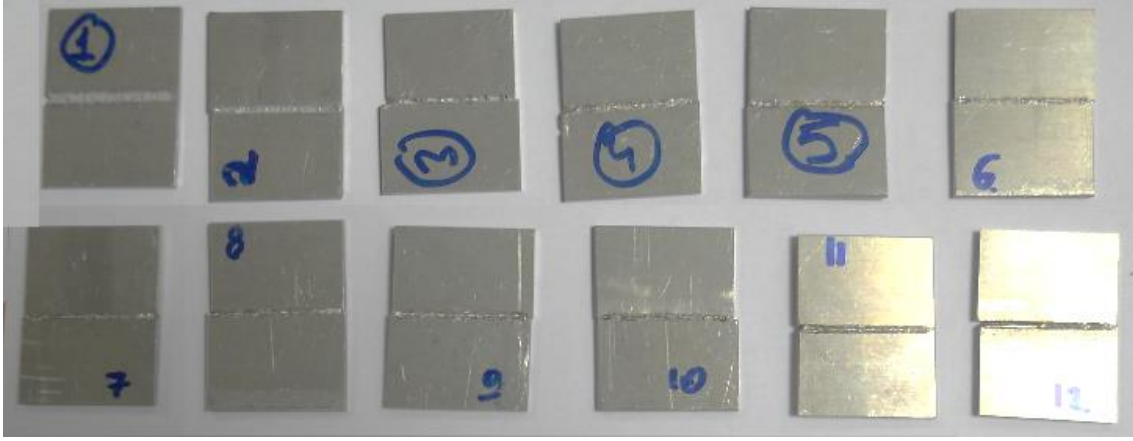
Bindirme kaynak bağlantılı laser kaynak dikişli numunelerden makro görüntüler
